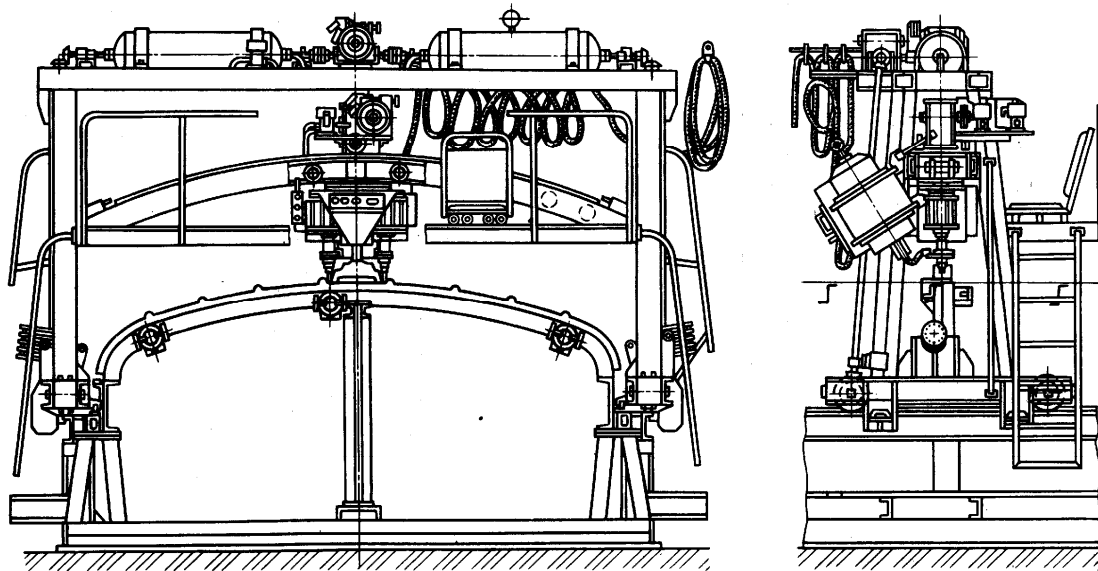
Самоходная двухэлектродная контактная машина для сварки секции крыши
